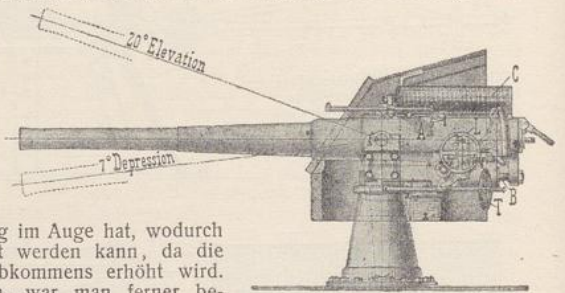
A Wiege. B Hydraulischer Bremszylinder. C Ausrennfedern. L Höhen-, T Seitenrichtmaschine.
